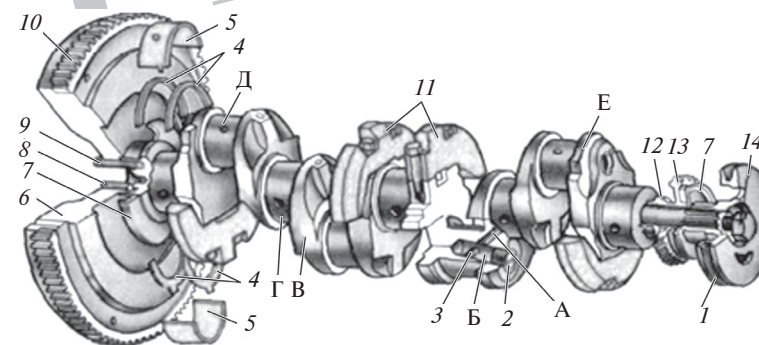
Коленчатый вал двигателя Д-245 с сопряженными деталями:
